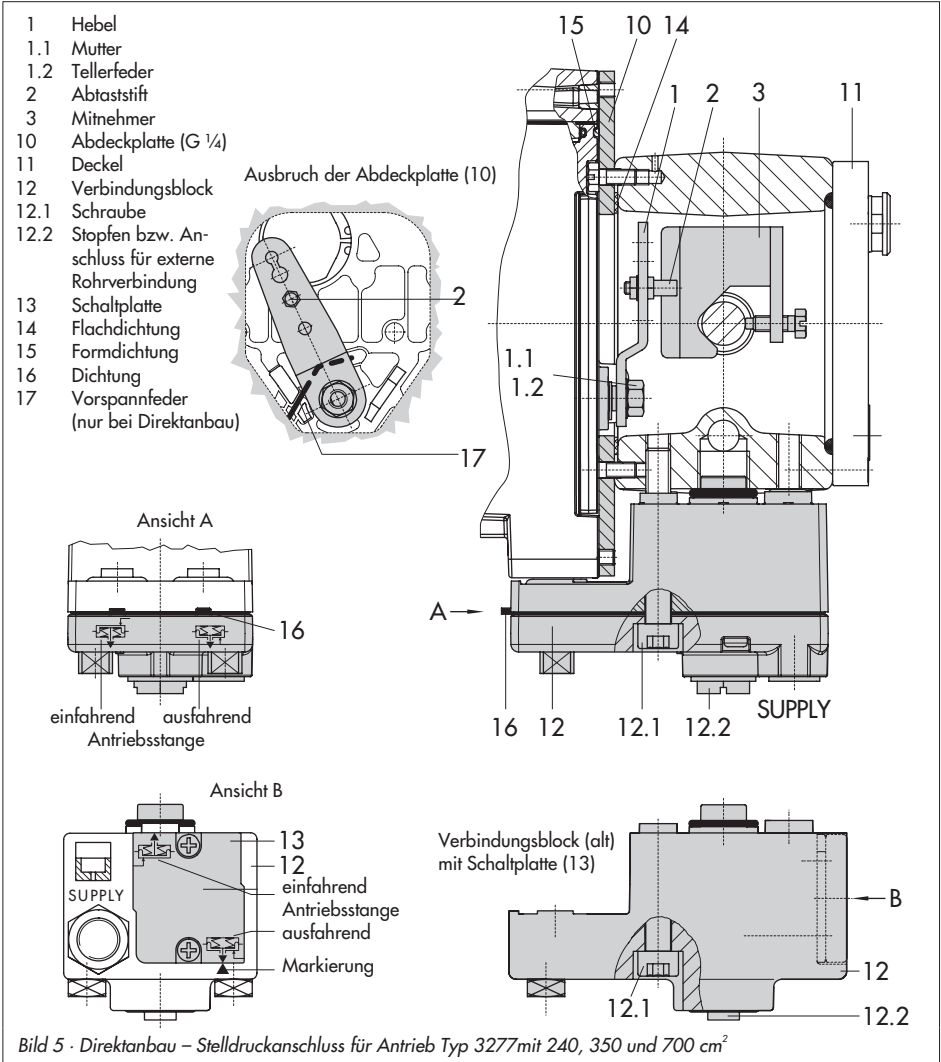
· Direktanbau – Stelldruckanschluss für Antrieb Typ 3277 mit 240, 350 und 700 cm<sup>2</sup>
